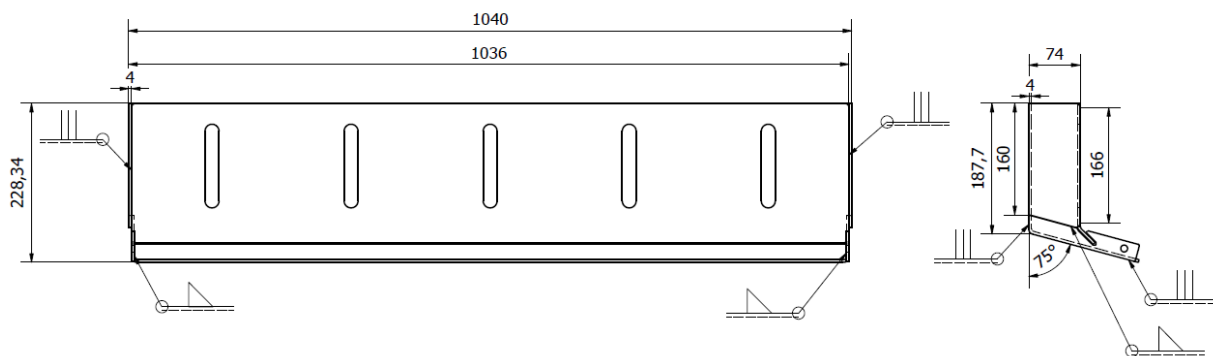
Representação do esquema de soldadura do reservatório, medidas em milímetros e simbologia normalizada para soldadura.
